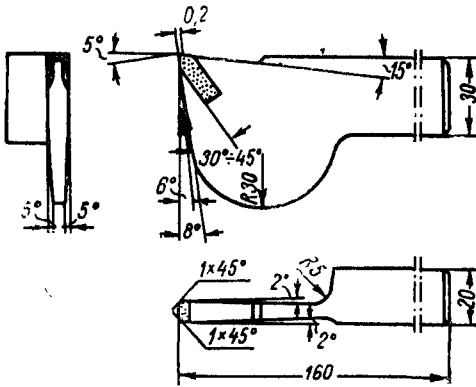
Отрезной твердосплавный резец конструкции В. И. Гургаля.
